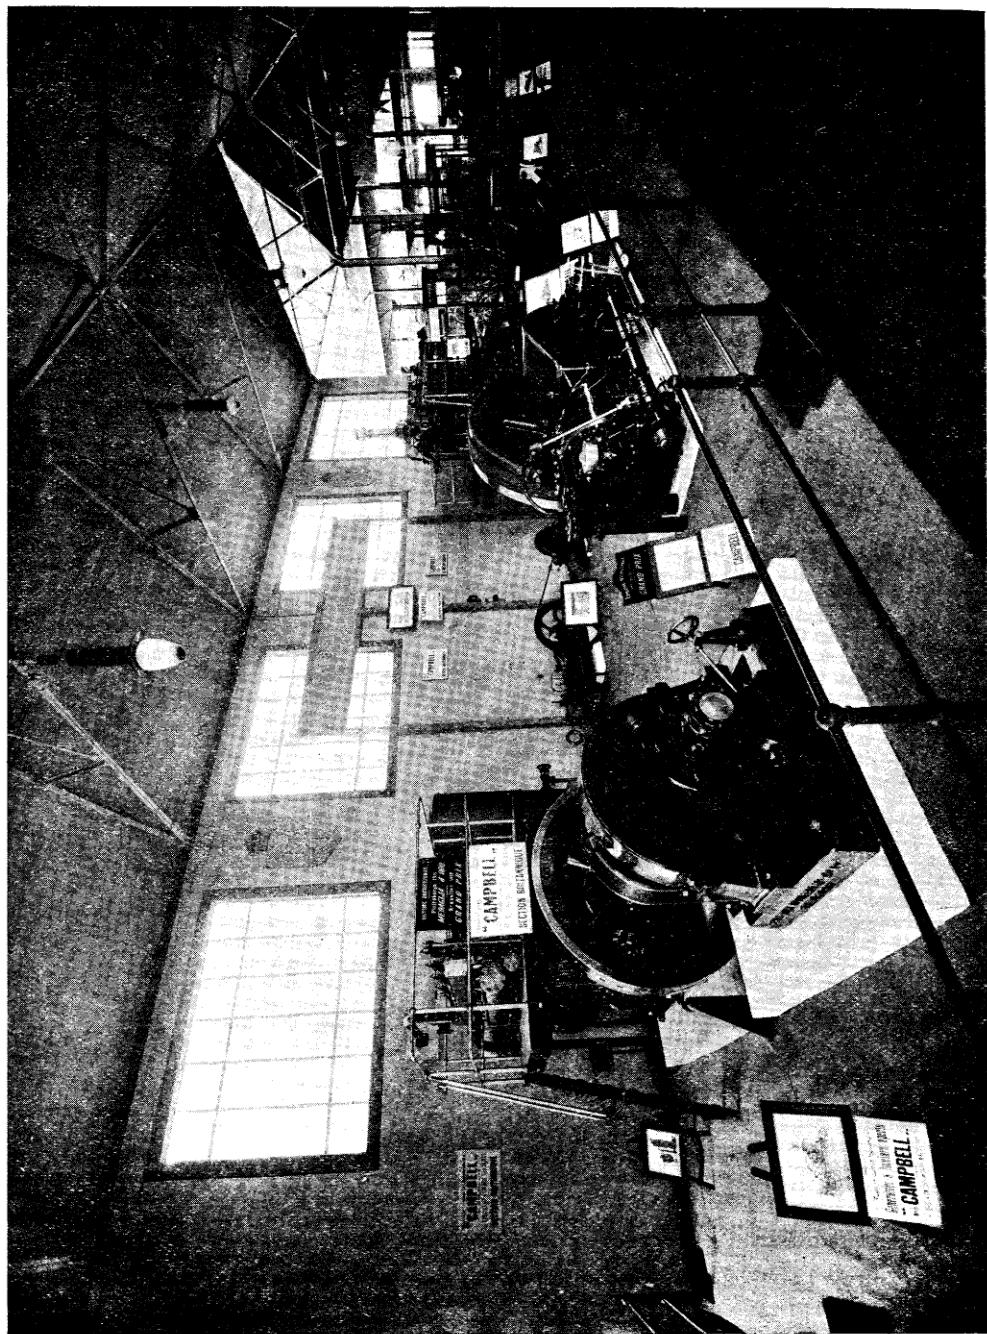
Vue du stand de la Société « The Campbell Gas Engine Co » de Halifax
